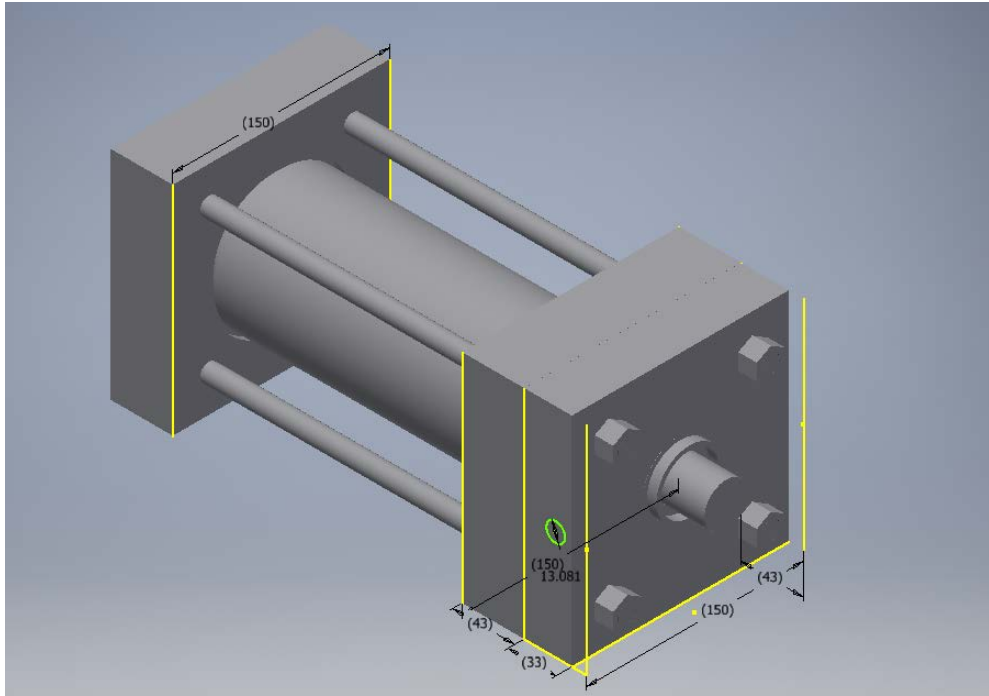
Ensamble del cilindro en vista isométrica.
